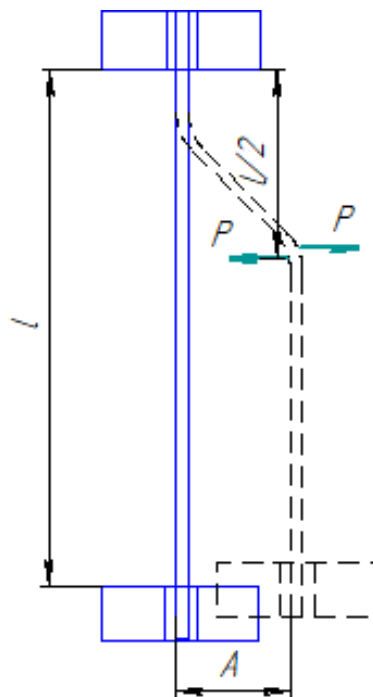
Розрахункова схема підвіски кріплення решітного кузова зерноочисного агрегату СЗК-25
